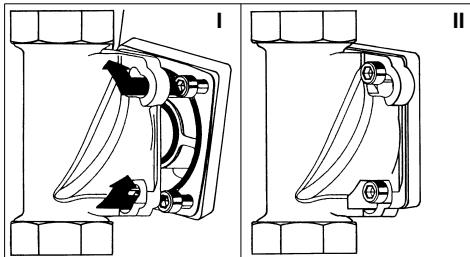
Einbaudrehflansch mit Bajonettsicherung
